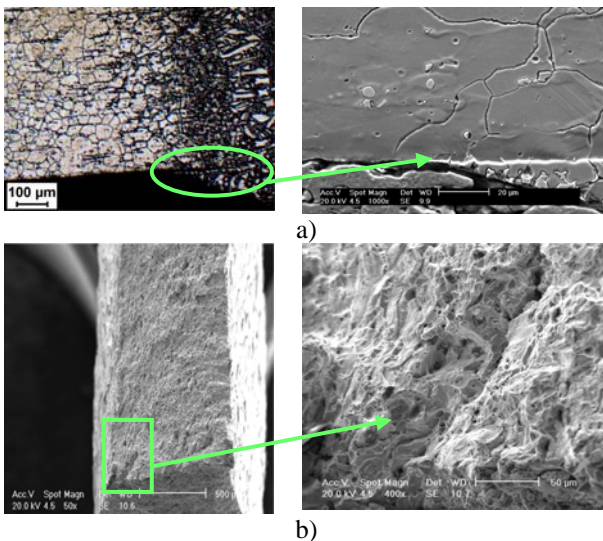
a) Defecto de soldadura en una de las muestras, b) formación de una grieta a partir del defecto de soldadura.
